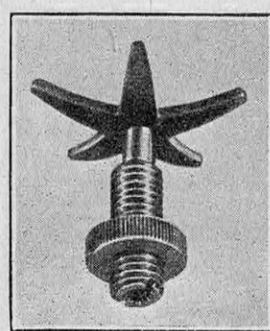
DÉTAIL DU SUPPORT DE LA TIGE FILETÉE ET DE LA BAGUE DU DISPOSITIF ANTIVOL POUR DOUILLES A VIS
